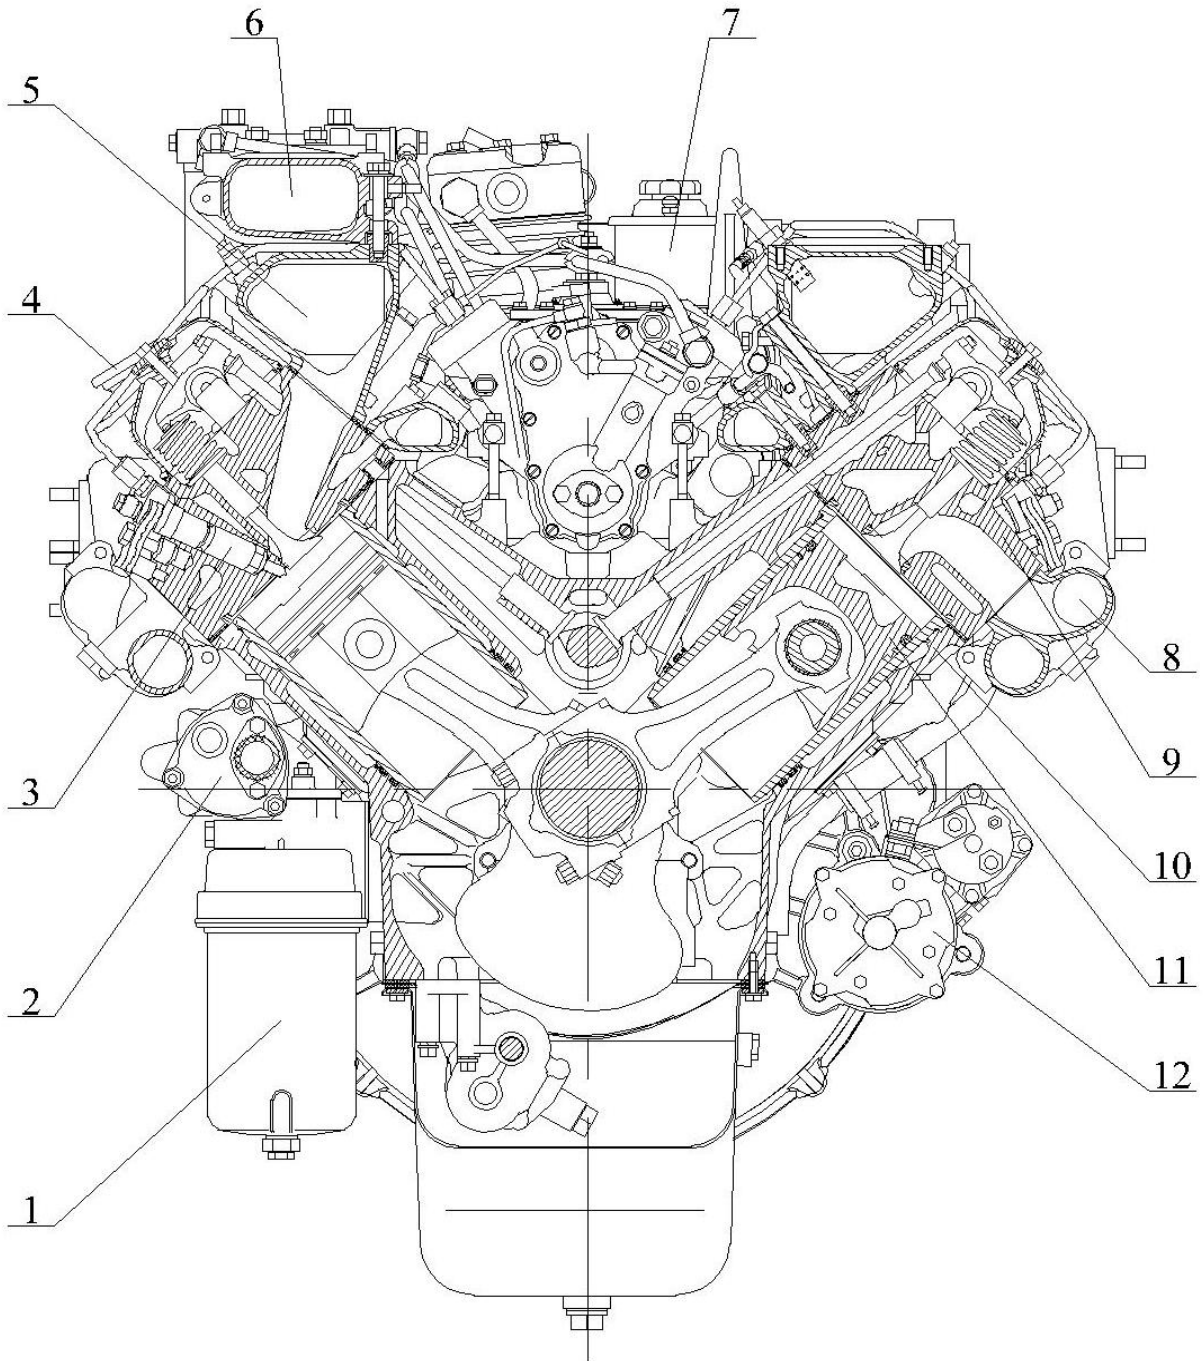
Поперечный разрез двигателя с V-образным ГНВД «ЯЗДА»: 1 – фильтр масляный; 2 – жидкостно–масляный теплообменник; 3 – форсунка; 4 – патрубок маслоналивной; 5 – коллектор впускной; 6 – труба подводящая; 7 – насос рулевого усилителя; 8 – коллектор выпускной; 9 – головка цилиндра; 10 – блок цилиндров; 11 – поршень; 12 - стартер
